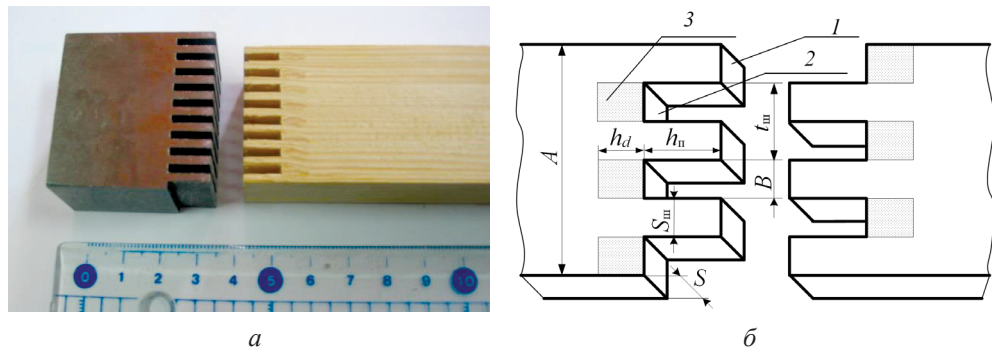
Внешний вид (а) и параметры прессованной заготовки (б): 1 – шип; 2 – проушина; 3 – деформированная зона;  $h_d$  – глубина деформированной зоны;  $A$  – ширина заготовки
